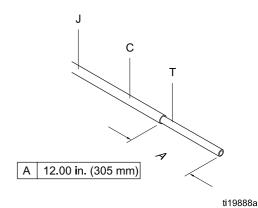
Dimensiones de la manguera sin carcasa 24M733 en el recinto WB100
